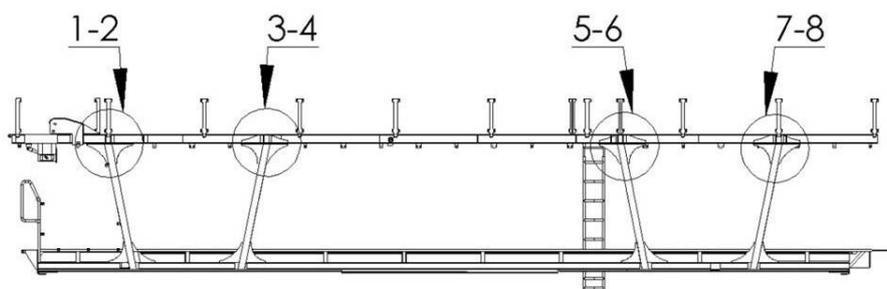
Puntos en los que se comprueba la soldadura.
